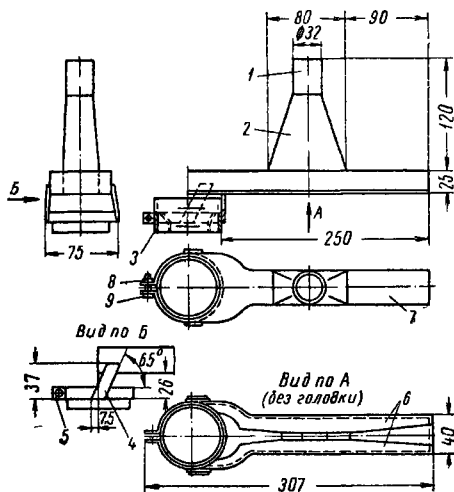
Местный пылегазоприемник ВЦНИИОТ для автоматической сварки под флюсом
